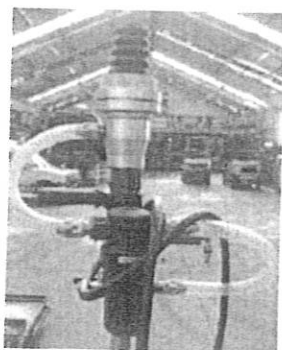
Foratore aspiratore per coppa olio motore cambio.
